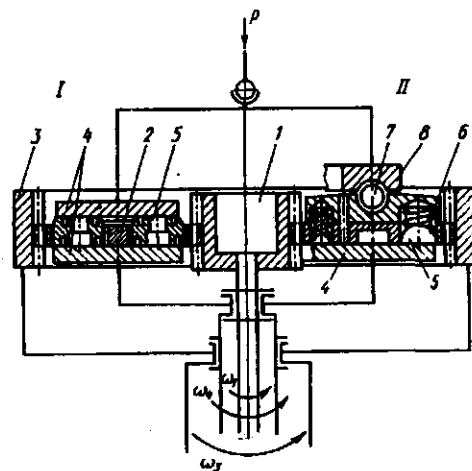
Наладка планетарного исполнительного механизма двухдискового доводочного станка при односторонней (II) и двусторонней (I) доводке: 1 – центральное колесо планетарного исполнительного механизма; 2 – кассета; 3 – наружное колесо планетарного исполнительного механизма; 4 – верхний и нижний притиры; 5 – деталь; 6 – пружина; 7 – шарнир; 8 – планшайба нагрузочного устройства
